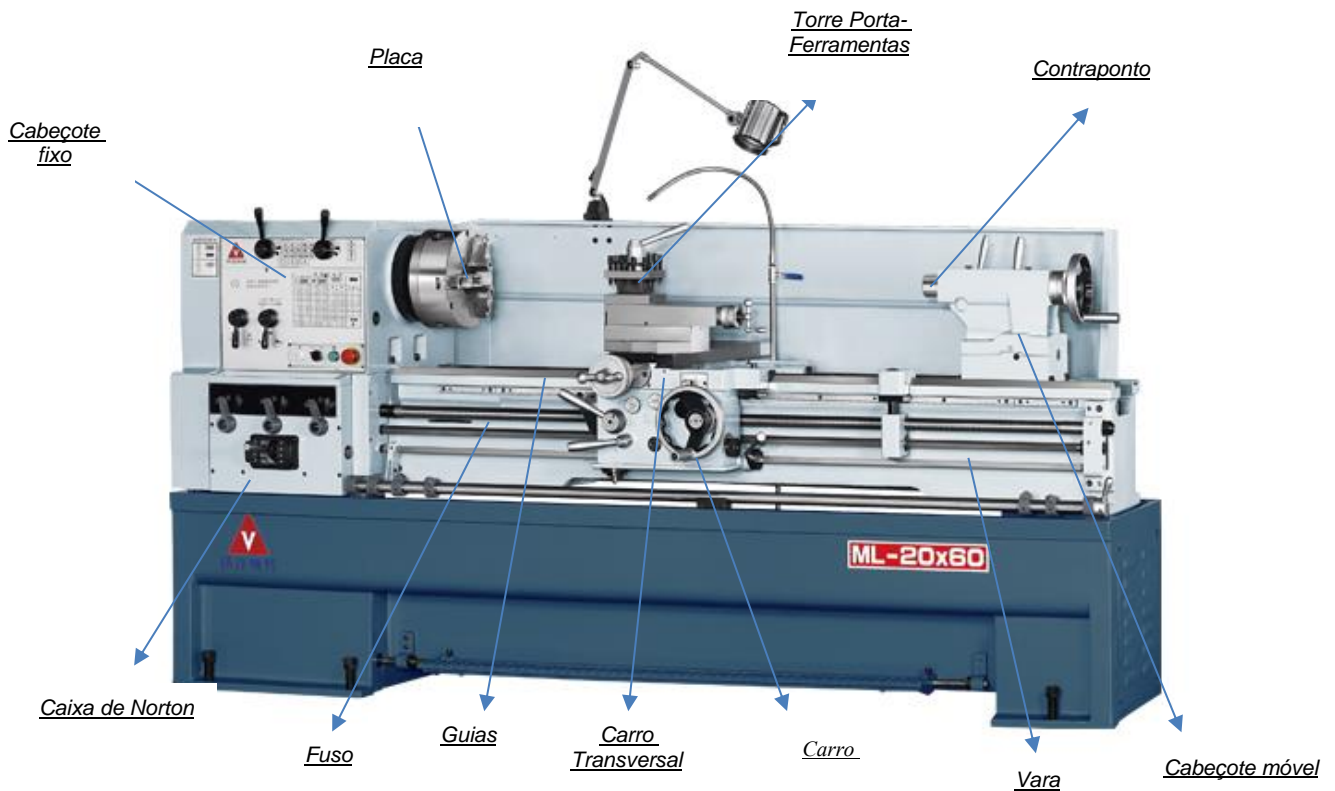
Torno mecânico e seus constituintes (adaptado) [28]
